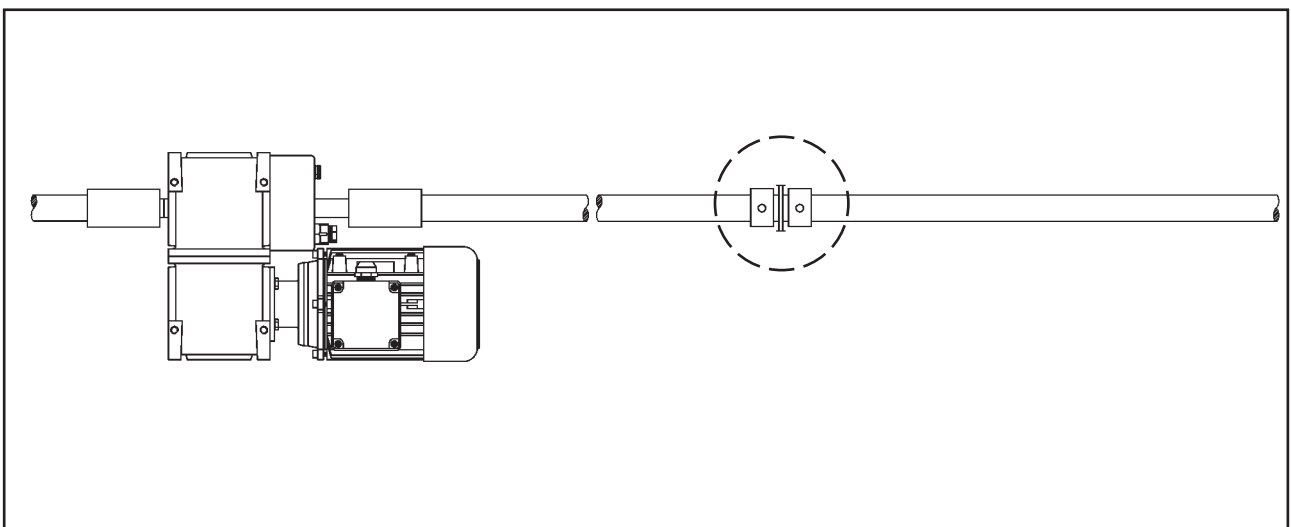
Stopringe med leje til begrænsning af aksial vandring.
